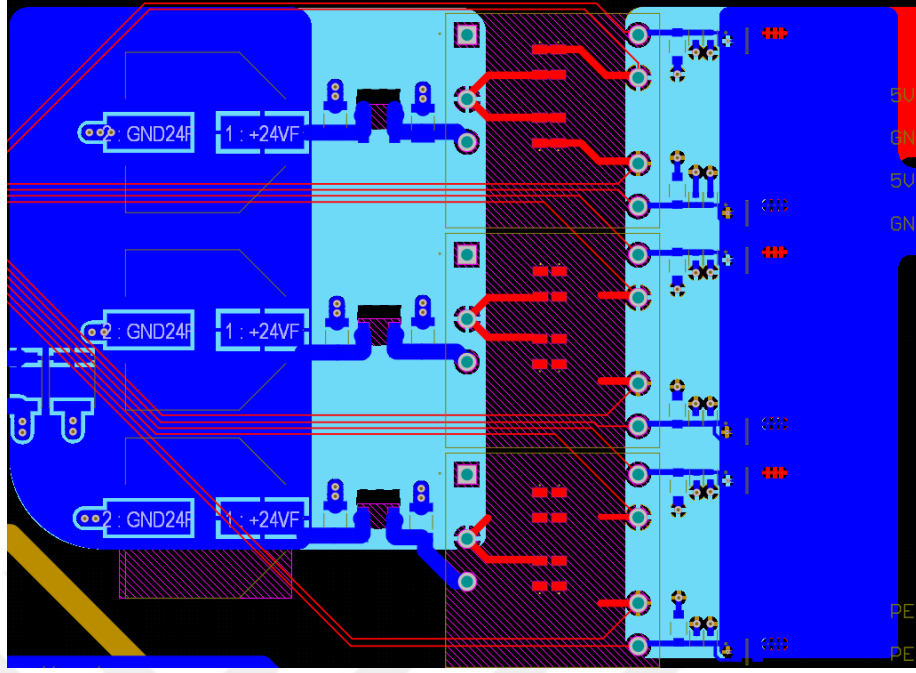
14: Koruma sistemi PCB yollandırılması.
